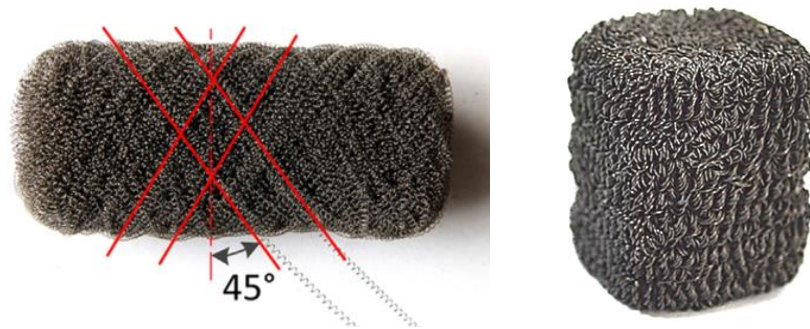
Pad fabricado mediante hilo metálico espiral antes de la compresión en el molde (izquierda) y después de la misma (derecha)
